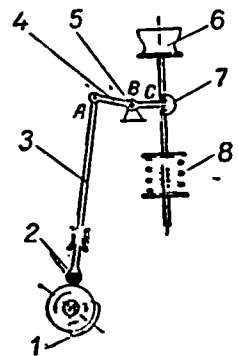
Парораспределительный механизм с кулачной шайбой.
